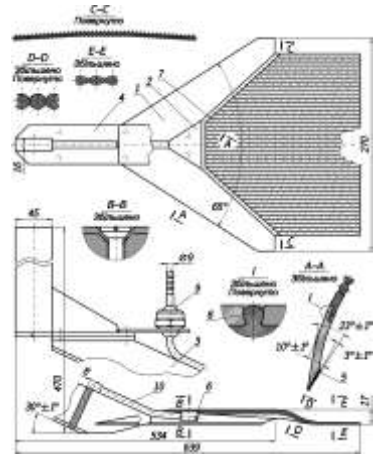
Розроблений робочий орган: 1 — леміш; 2 — склепіння; 3 і 4 — похила та вертикальна частини стояка; 5 — наплавлений шар; 6 — розпилювач; 7 — пружковий козирок; 8 — фіксатор козирка; 9 — індивідуальний фільтр-клапан-відсікач; 10 — трубопровід
